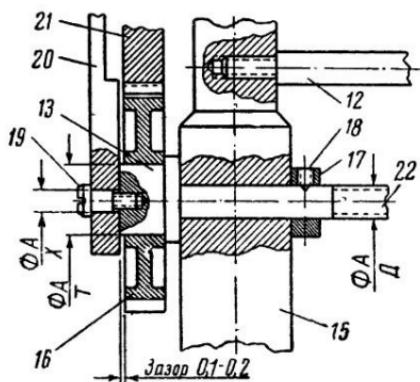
Модель механизма подачи суппорта токарного станка (схема узлов крепления «ходового винта», рычага «трензеля», направляющей «суппорта»): 12 — направляющая «суппорта»; 13 — «ходовой винт»; 15 — стойка; 16 — зубчатое колесо; 17 — стопорное кольцо; 18 — стопорный винт; 19 — винт крепления «трензеля»; 20 — планка; 21 — зубчатое колесо «трензеля»; 22 — ось зубчатого колеса.
